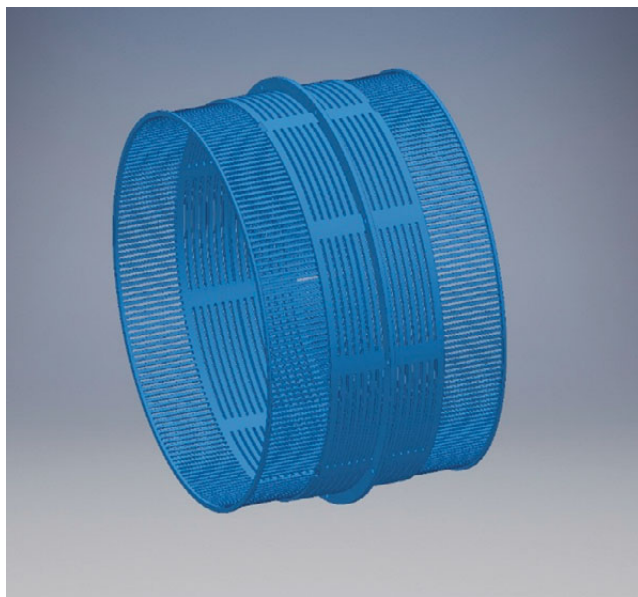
Внешний вид подвижного цилиндра клапанного узла
